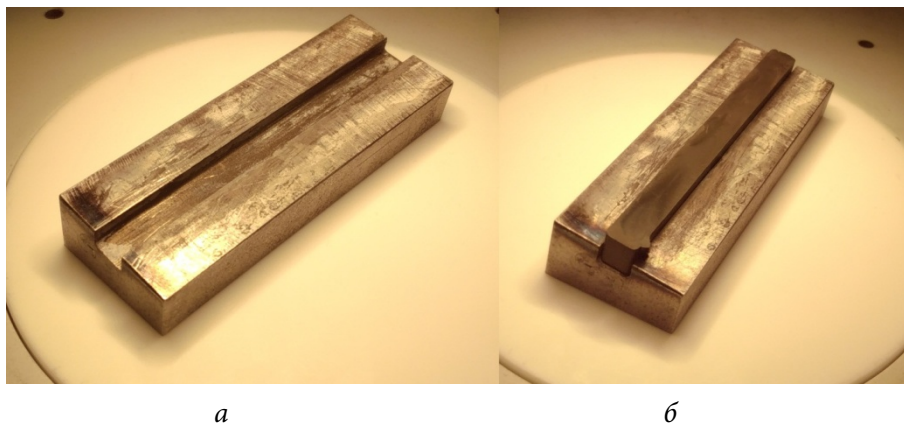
Полуформы: без обрабатываемого образца (а) и с обрабатываемым образцом «зеленой» детали (б)
